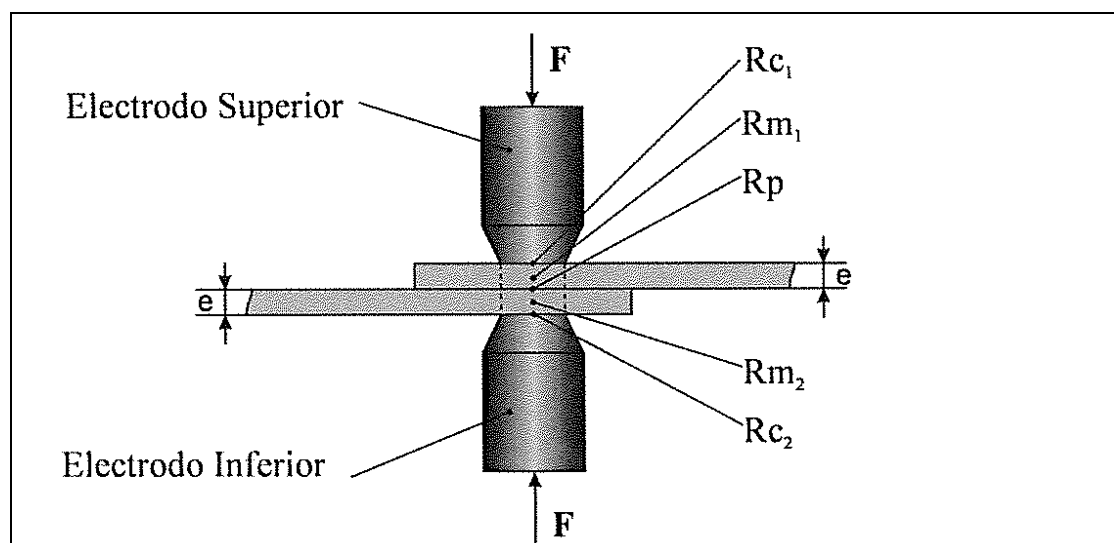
Resistencias presentes en un proceso de soldadura por puntos
